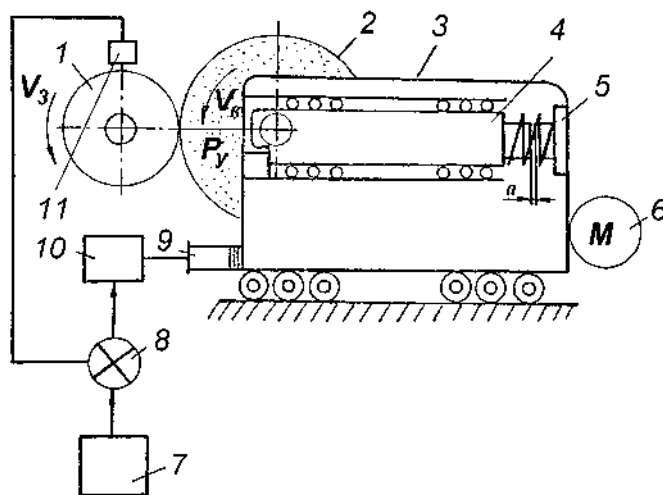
Схема, позволяющая повысить точность шлифовальной обработки
